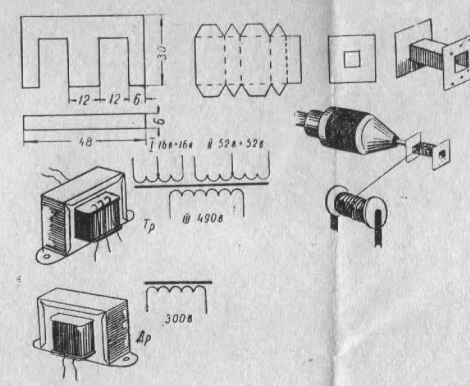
Детали и способ изготовления трансформатора и дросселя для преобразователя второго типа
